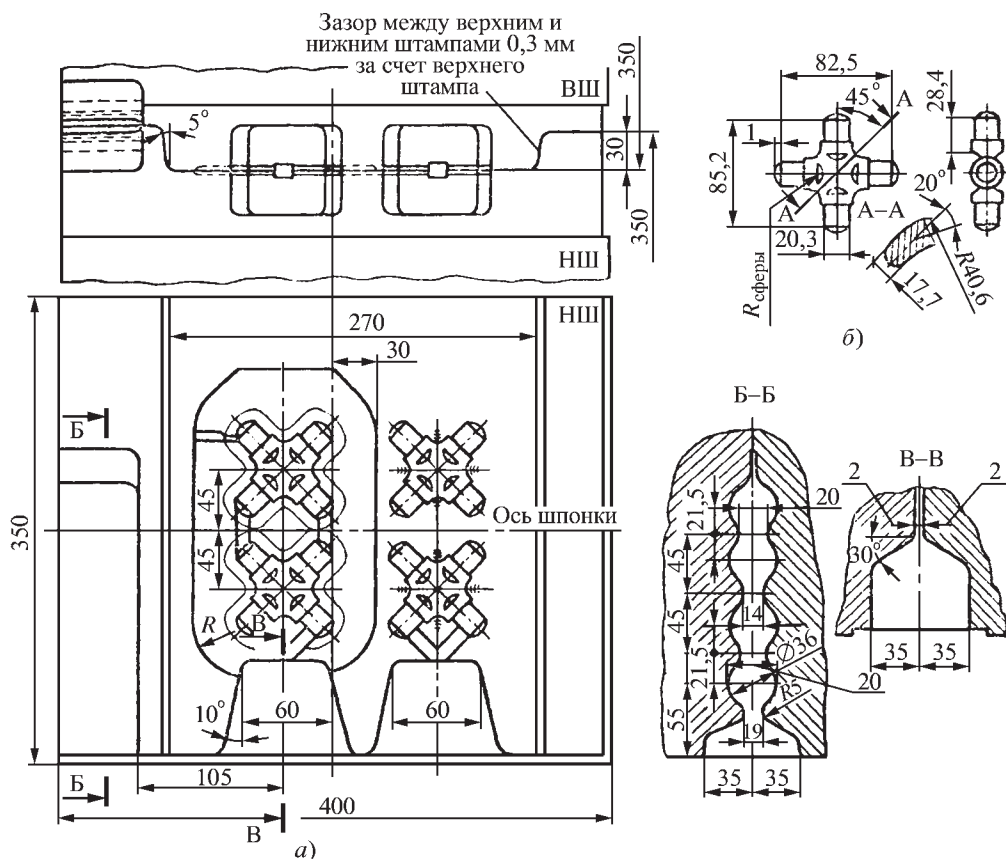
Молотовой штамп (а) и горячая поковка (б) крестовины:
